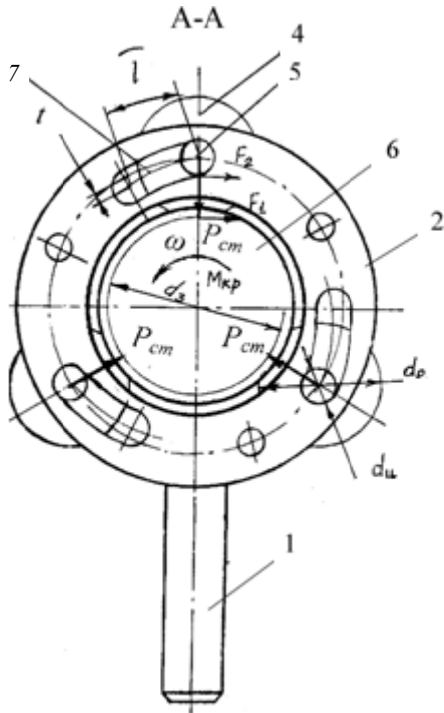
Разрез А-А охватывающего инструмента для статико-импульсного упрочнения впадины резьбы на заготовке с предварительно нарезанной резьбой
